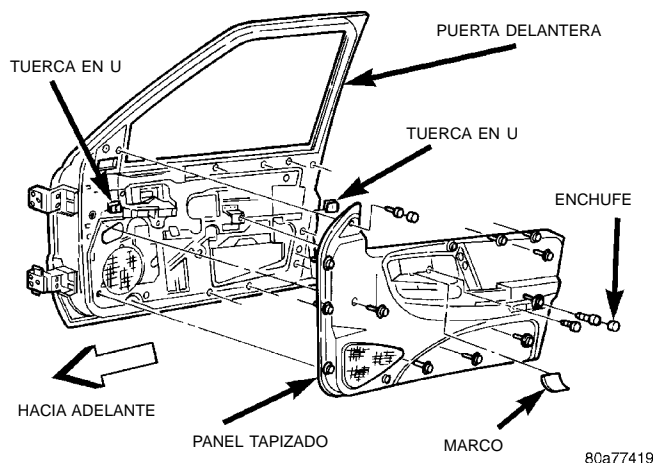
Desmontaje/instalación del panel tapizado de la puerta delantera
